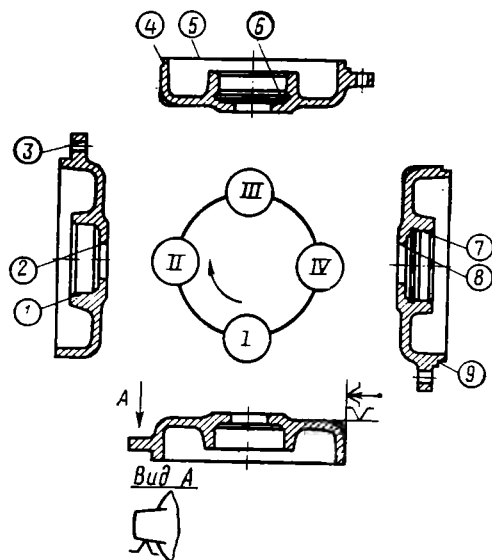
Четырехпозиционный агрегатный станок для обработки подшипниковых щитов
